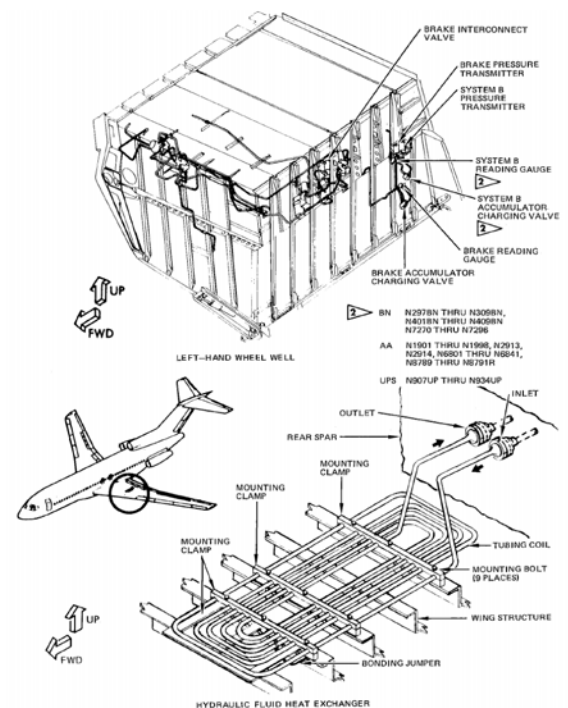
Sistema hidráulico B – Locación del equipo 2/2 (Fuente: B727-AMM)
